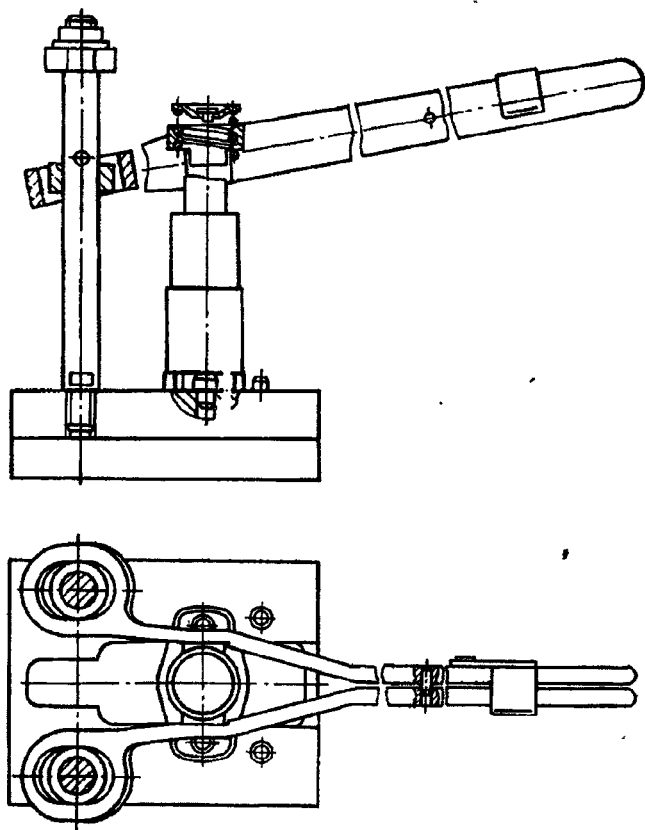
Установка насосной секции ТНВД в приспособление И801.20.000 для разборки-сборки
